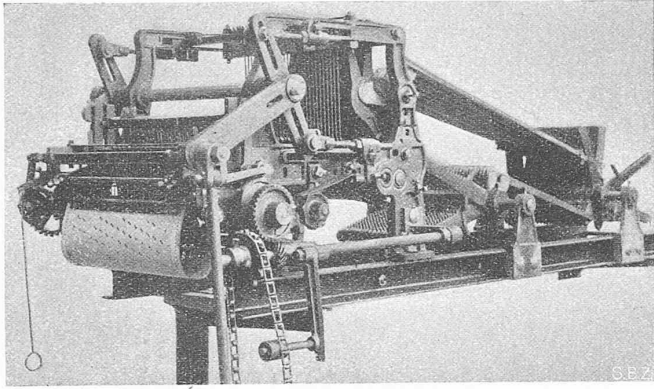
Schaffmaschine mit Papierdessin. Gebr. Stäubli & Cie., Horgen.
